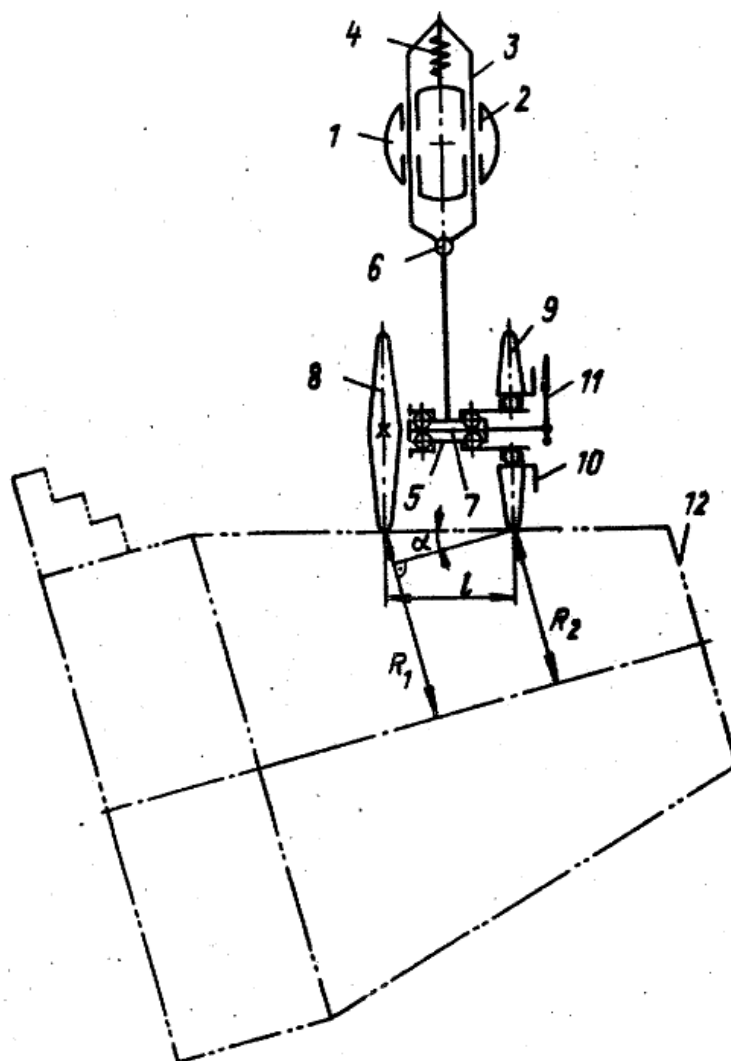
Пристрій для вимірювання зовнішнього конуса
